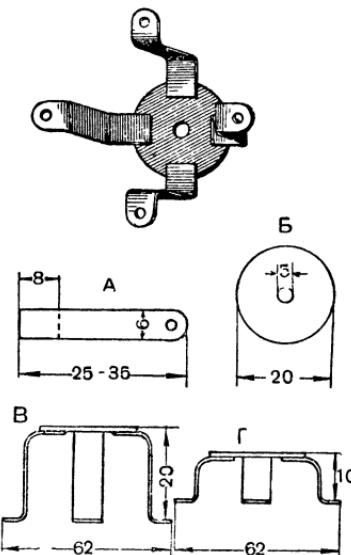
Щит для шарикоподшипников (второй вариант): А — заготовка лапки; Б — центральный кружок; В — профиль переднего щита; Г — профиль заднего щита.
